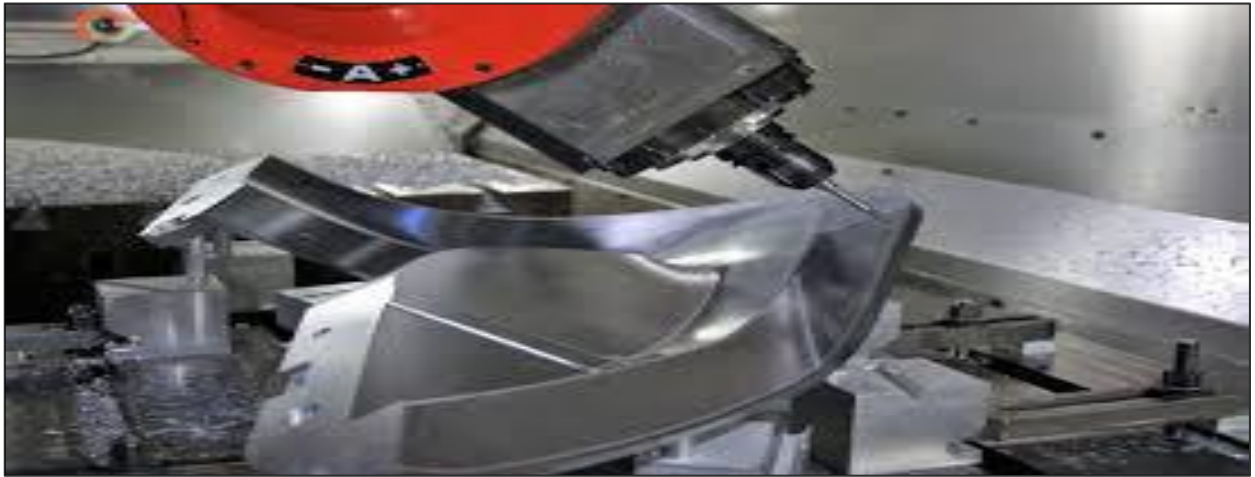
Usinage sur CNC d'un moule pour thermoformage .
